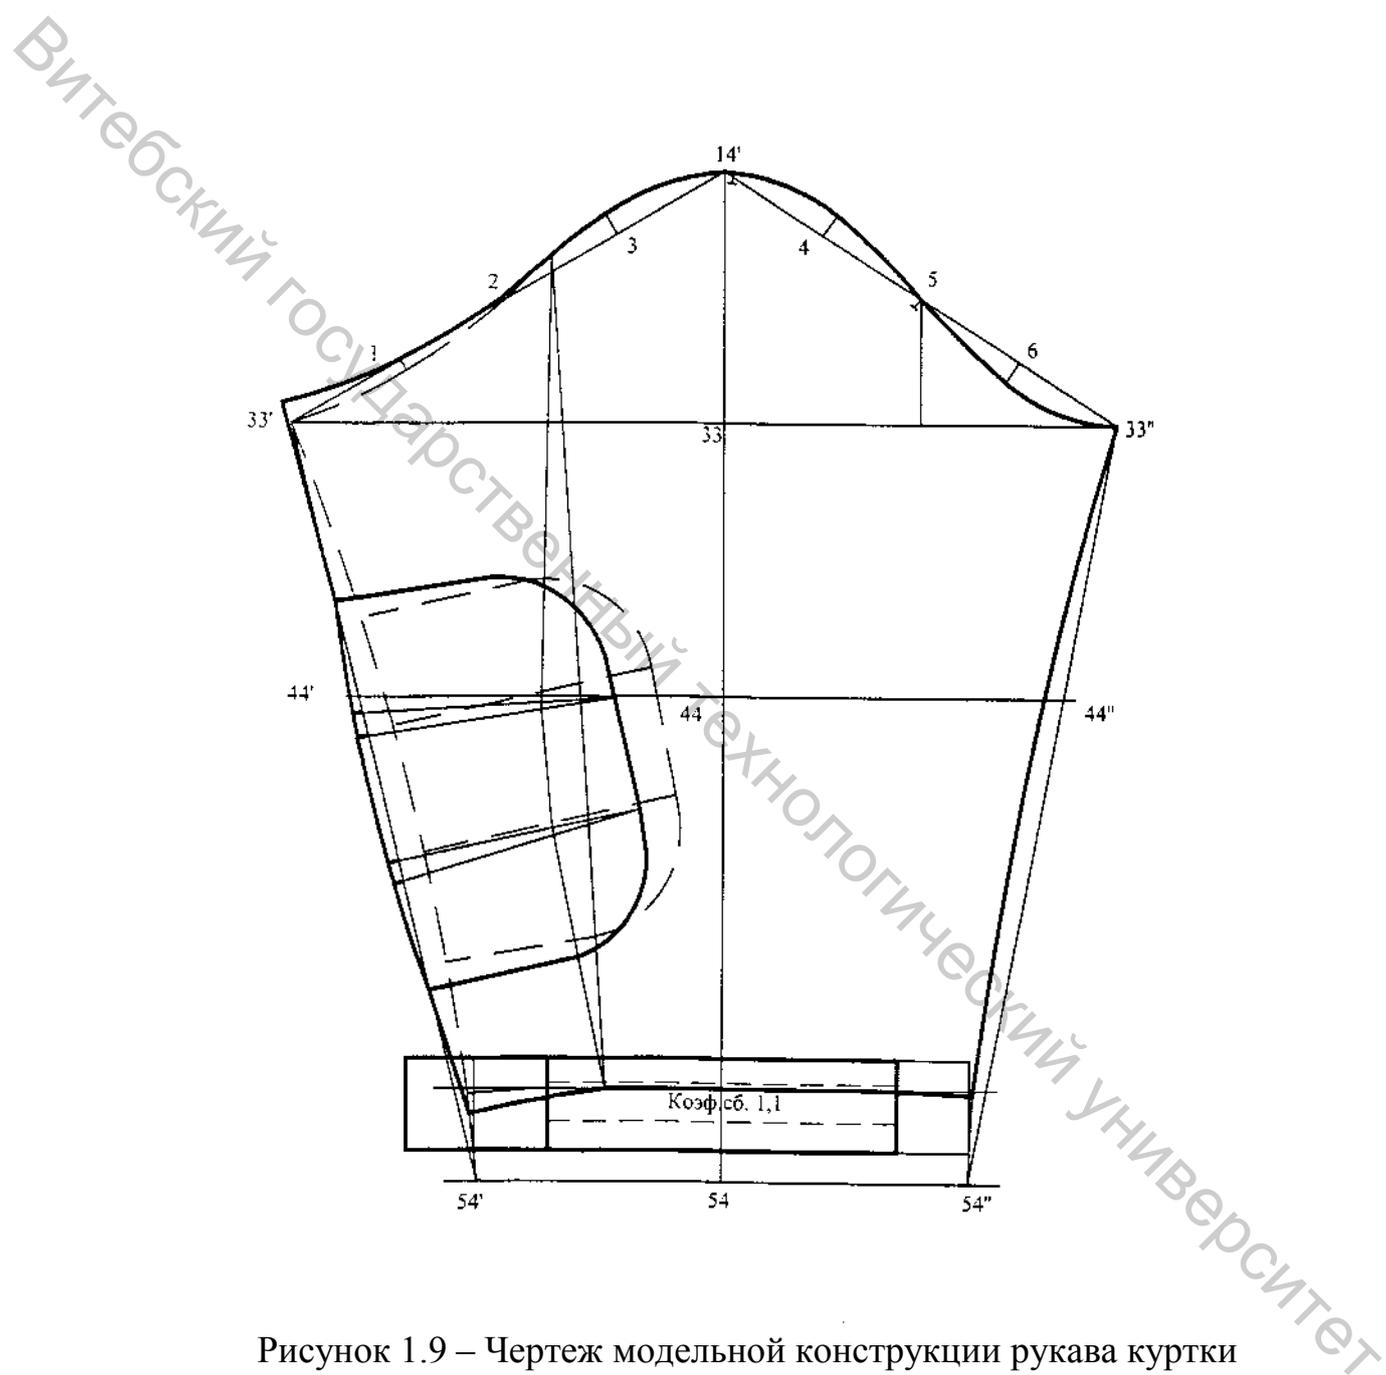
Чертеж модельной конструкции рукава куртки
